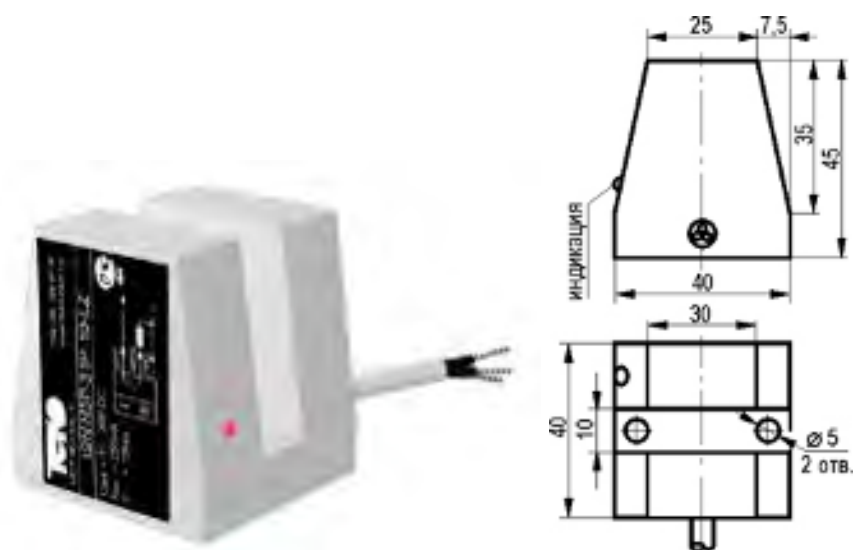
Общий вид и габаритный чертеж датчика ISN N3P-32N-10-LZ
